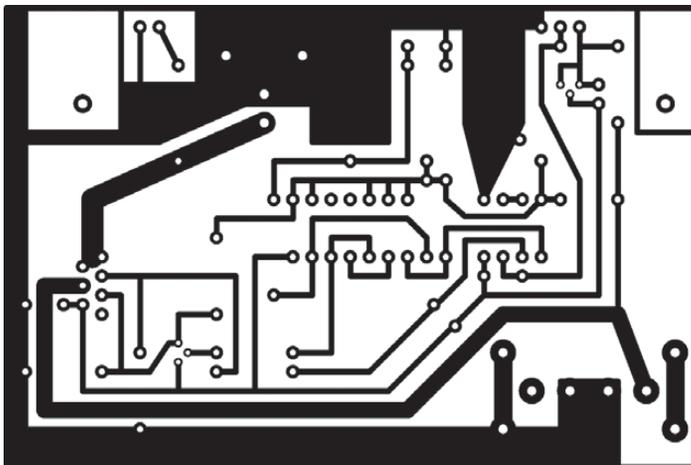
Leitungsführung der Platine für die Schutzschaltung 2; Abmessungen 92 mm × 61 mm, M 1:1
